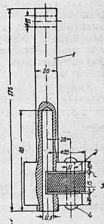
Процесс вывертывания шпильки головки блока цилиндров при помощи роликового экстрактора
